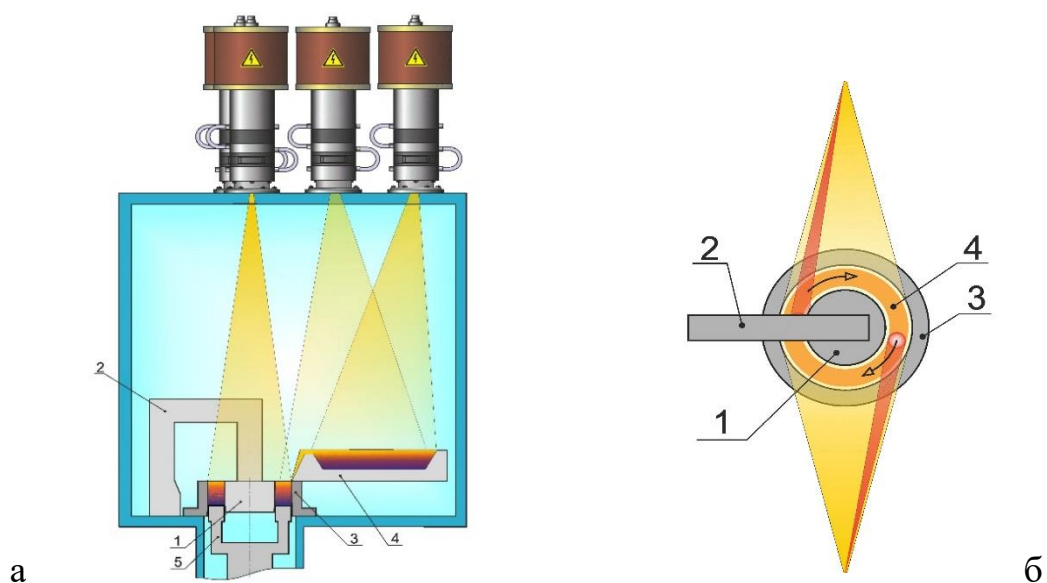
Схема конструкції пристрою для отримання трубчатої заготовки методом ЕПП (а); схема виду зверху нагріву розплаву ванни двома електронними гарматами з розгорткою променів у формі півкілець (б): (1 – водоохолоджуваний дорн, 2 - траверса; 3 - водоохолоджуваний тигель; 4 - проміжна ємність; 5 - водоохолоджуваний шток з хвостовиком)
